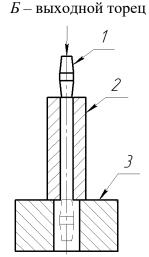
Схема модели и направление движения дорна: 1 — дорн; 2 — втулка; 3 — опора
